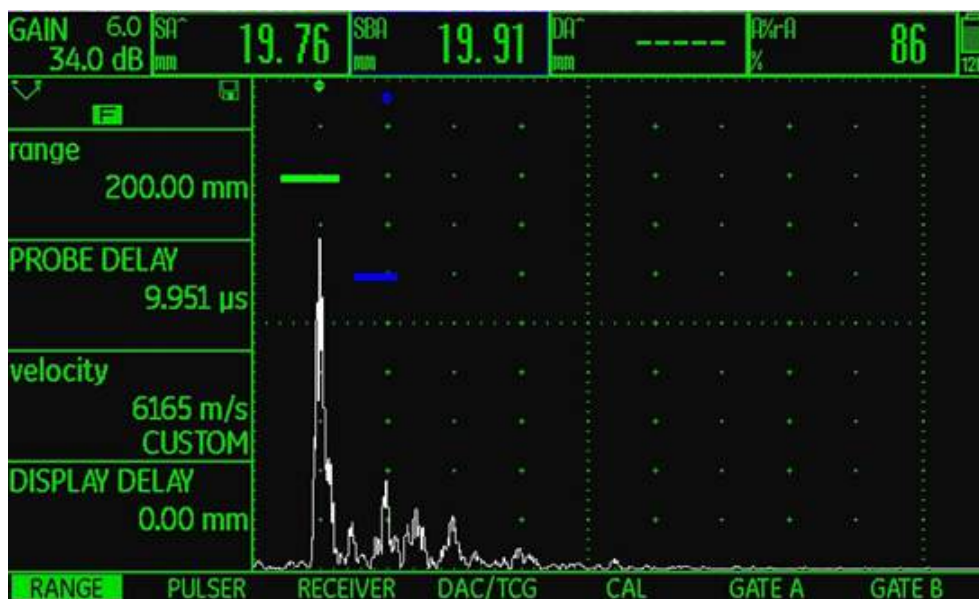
Sinal obtido aquando a inspeção com técnicas de ultrassons do provete L-03-5.
